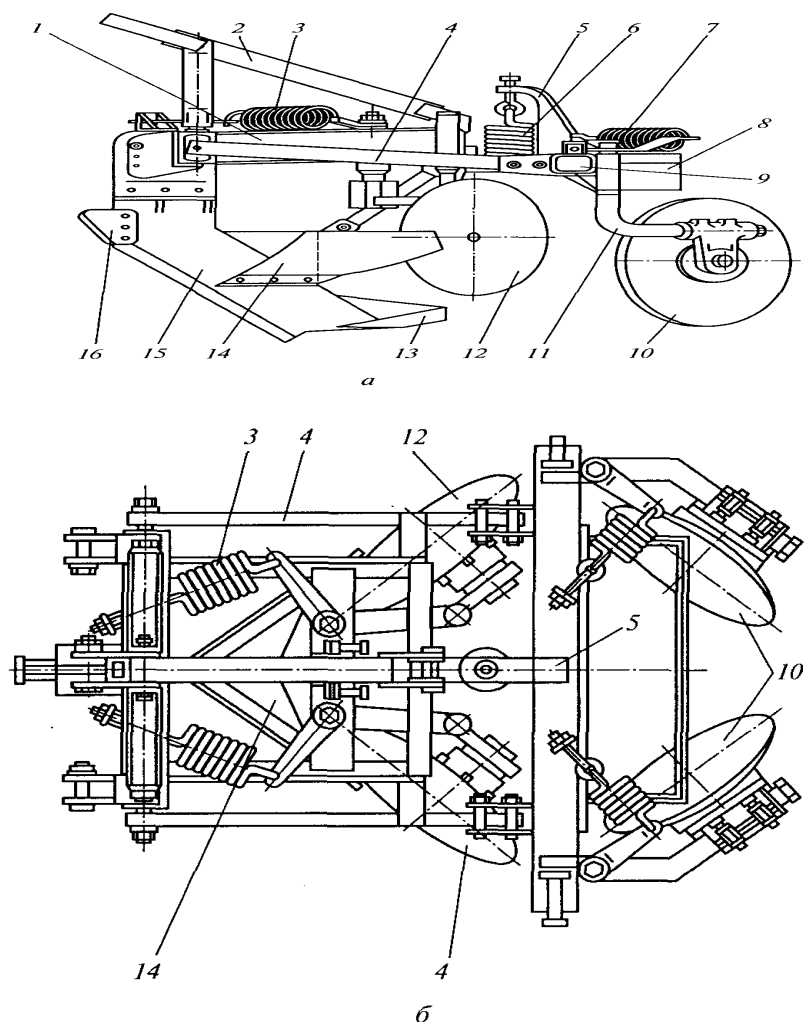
Плуг лесной дисковый ПЛД-1,2: *а* — вид сбоку; *б* — вид сверху; 1 — передняя рама; 2 — навесное устройство; 3, 6 и 7 — пружины; 4 — тяга; 5 — кронштейн; 8 — балластный ящик; 9 — задняя рама; 10 — задний дисковый корпус; 11 — коленчатая ось; 12 — передний дисковый корпус; 13 — рыхлительная лапа; 14 — дерноним; 15 — черенковый нож; 16 — лобовик
